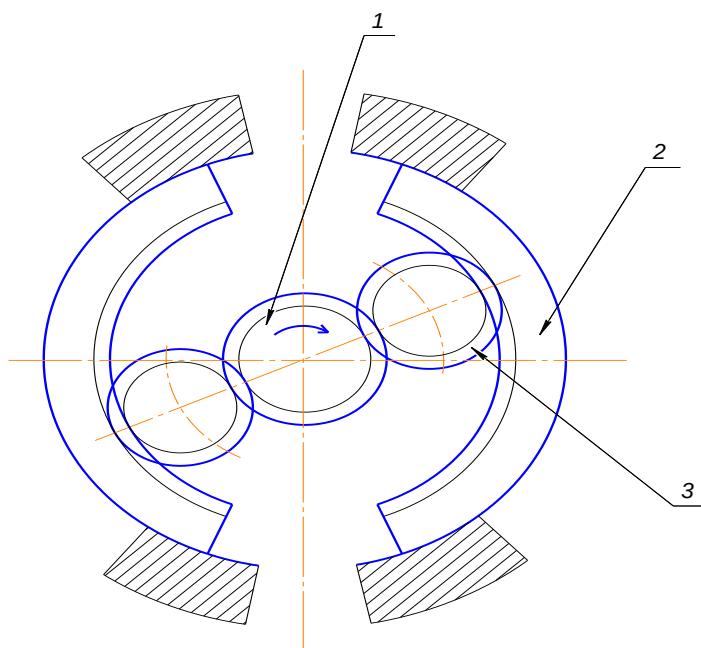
а – Планетарный процесс накатывания: 1 – неподвижные сегменты; 2 – вращающийся резьбовой ролик; 3 – обрабатываемые детали
